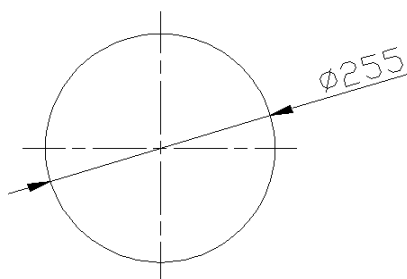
Construcción de la tapa plana del reactor de metoxido.
